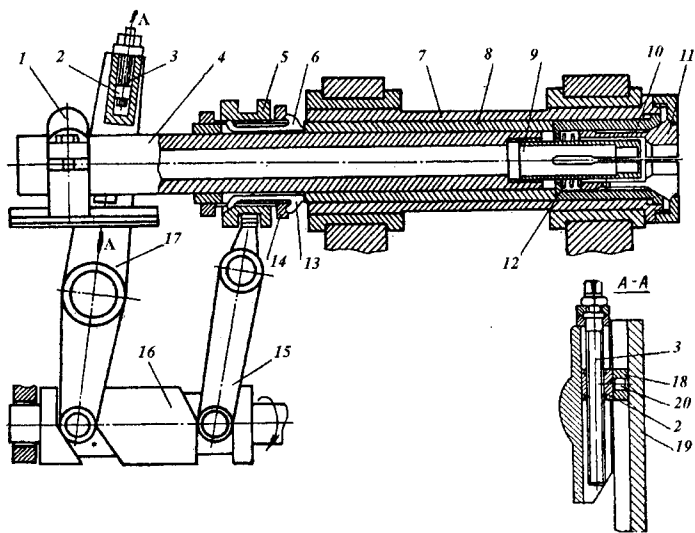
Схема цангового механізму подачі і затискання прутка токарного автомата
